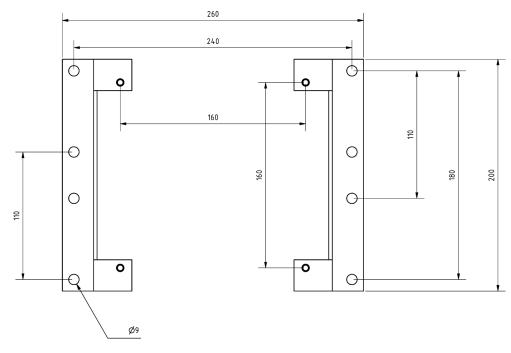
Padrão ângulo de fixação dimensões (mm)
